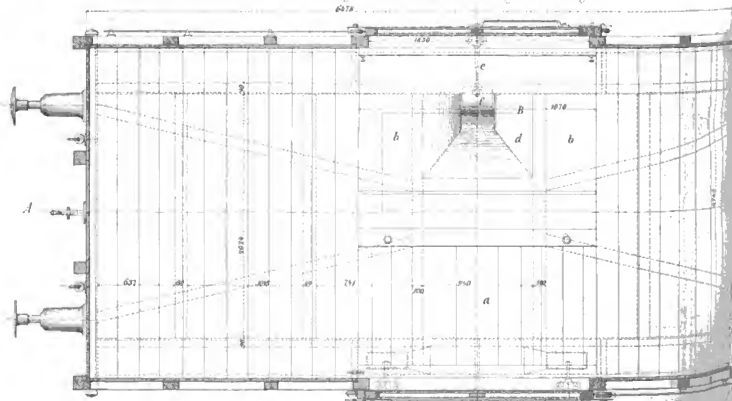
Grundriss der Einrichtung für gewöhnliche Güter.
